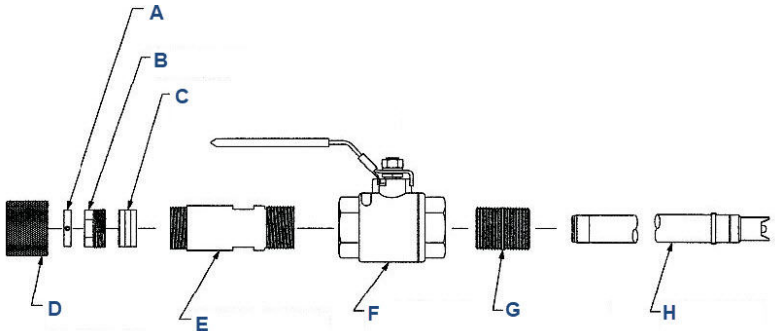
Kit del conjunto de válvula de bola (PN 23765-00) y sensor
